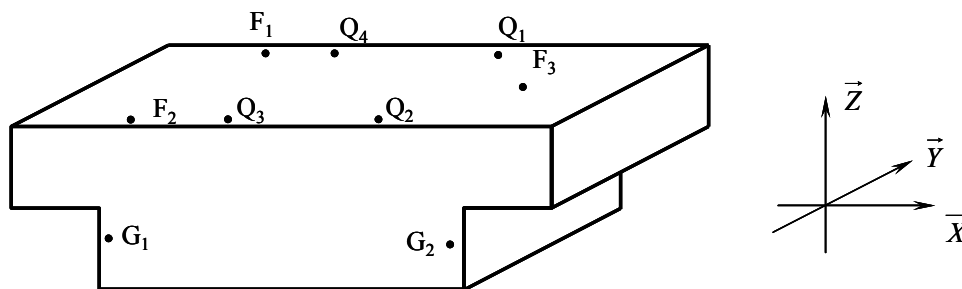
Points à contrôler sur la pièce avant usinage (Phase 20)
